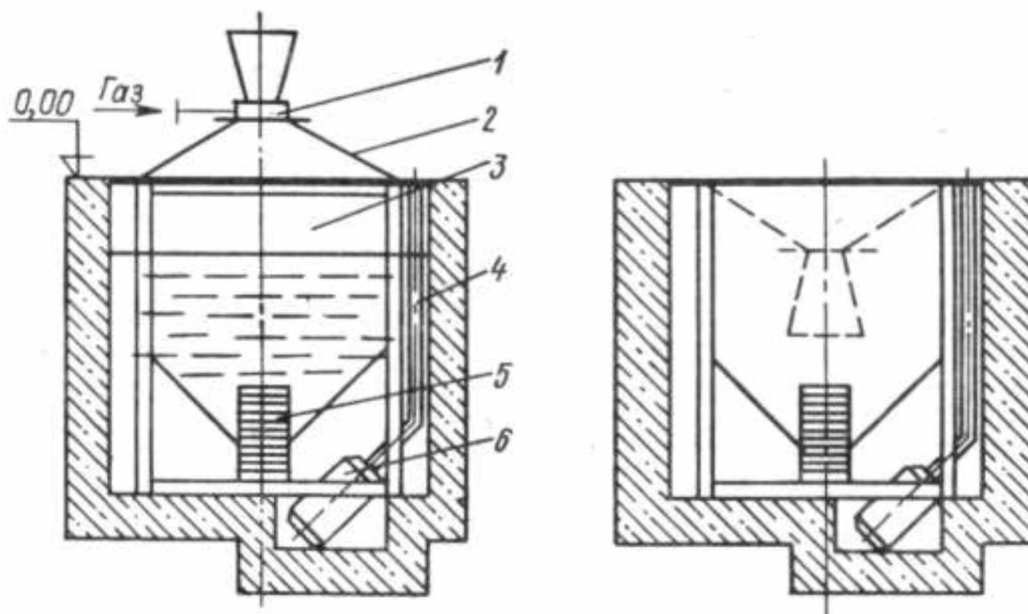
Схема малогабаритної установки для отримання металевого литого дробу
